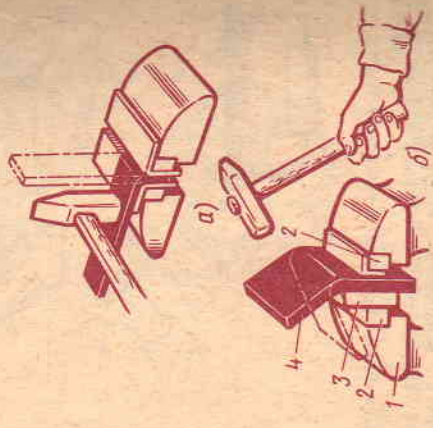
Гибка полосового металла в слесарных тисках под прямым углом (а) и на оправке (б): 1 — тиски, 2 — губки, 3 — оправка, 4 — заготовка
